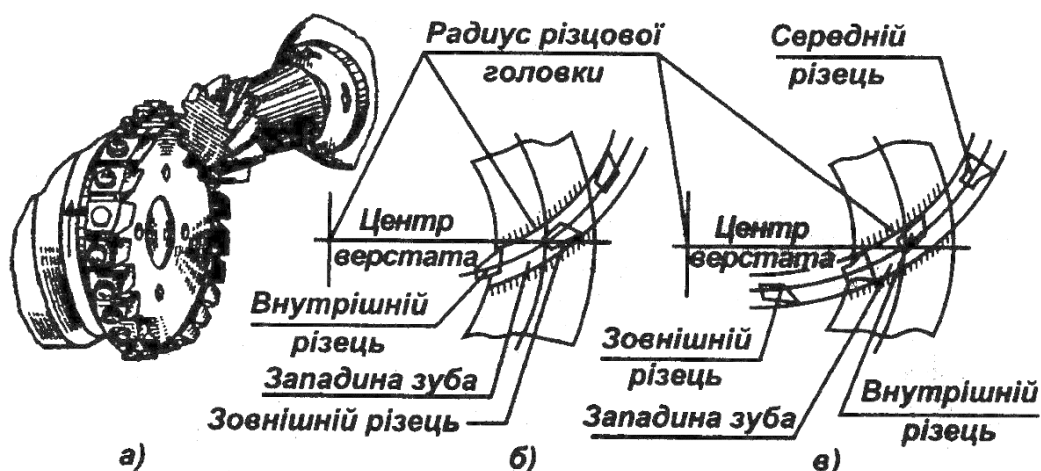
Схеми нарізання конічного зубчастого колеса з криволінійними зубами
